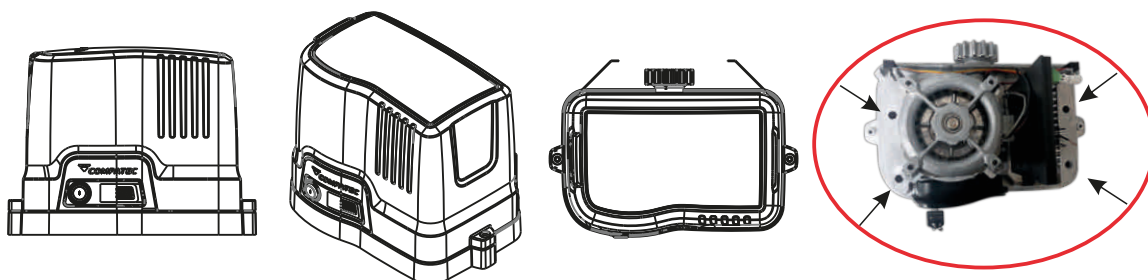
Para fixar as base do Kit ao corpo do Movimentador Deslizante e necessário remover a tampa.
